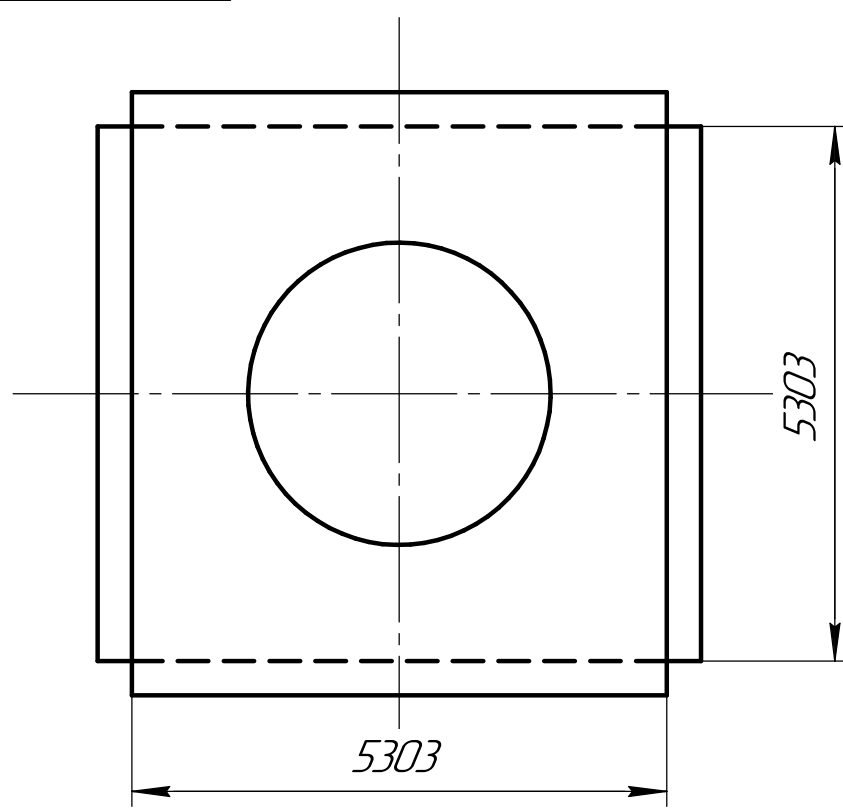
Габаритно-компоновочный эскиз ПГК
